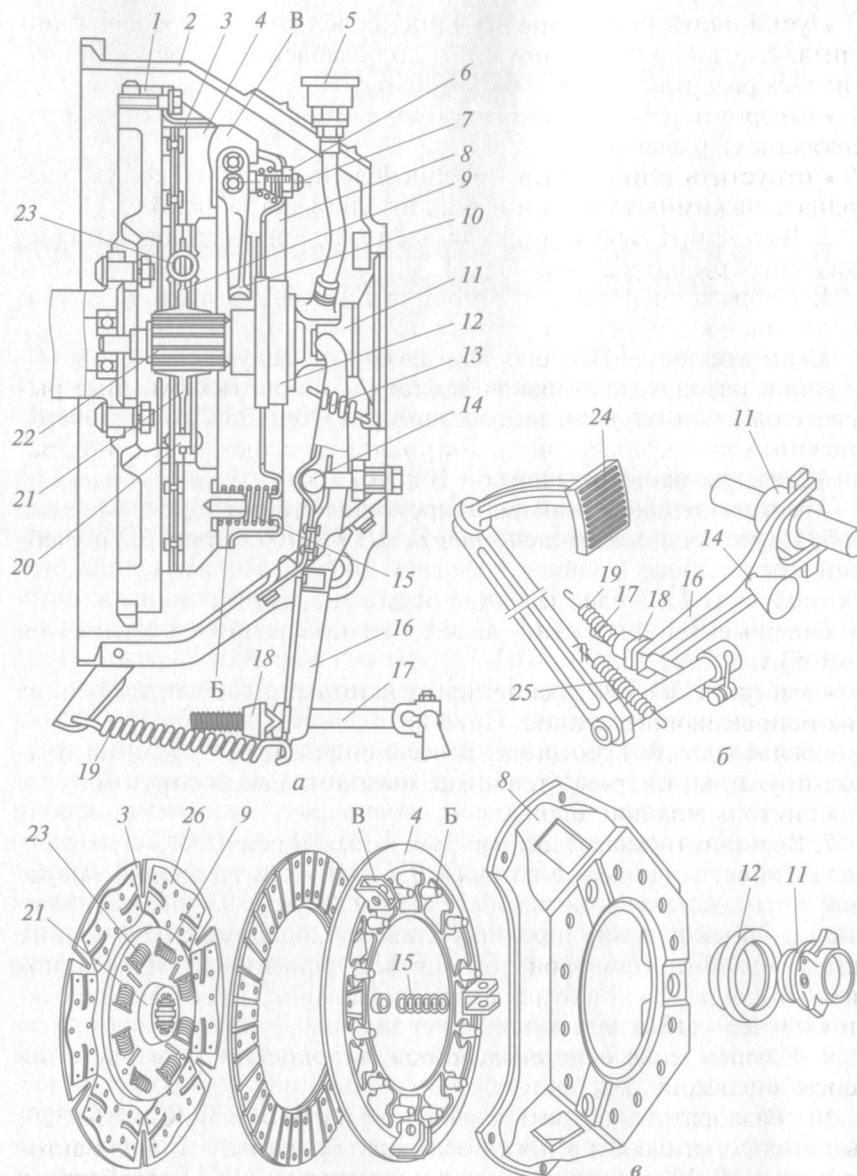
Сцепление автомобиля ГАЗ-53А:
